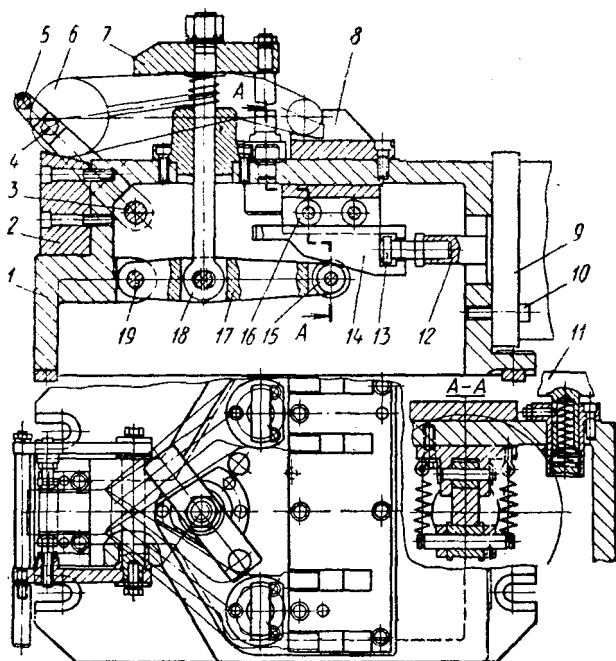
Приспособление для крепления рычагов при одновременном фрезеровании двух торцов бобышек
